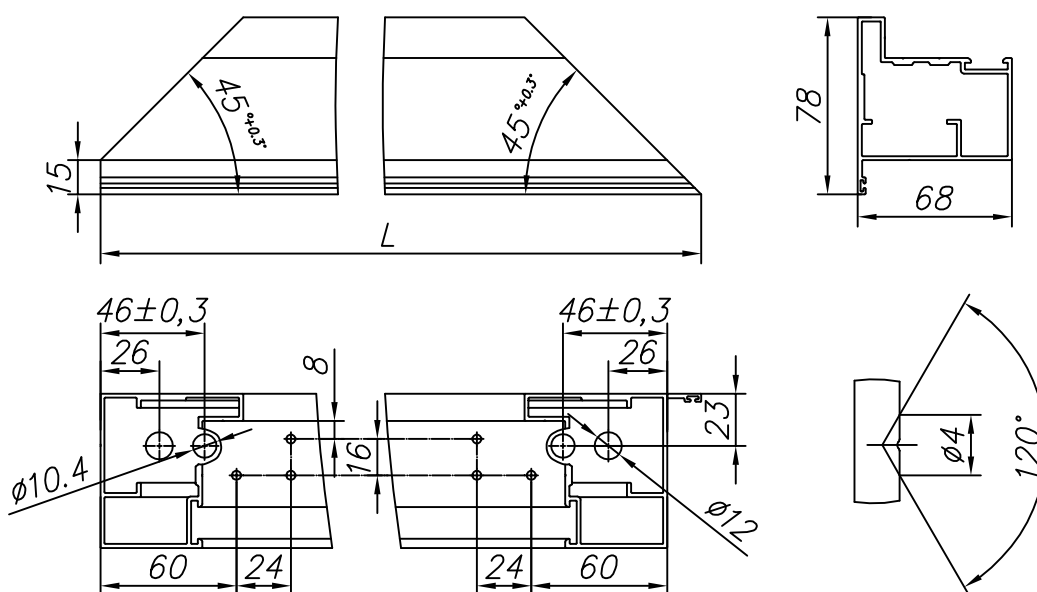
Изготовление стойки без паза для замка из профиля FLGU.400.0108
